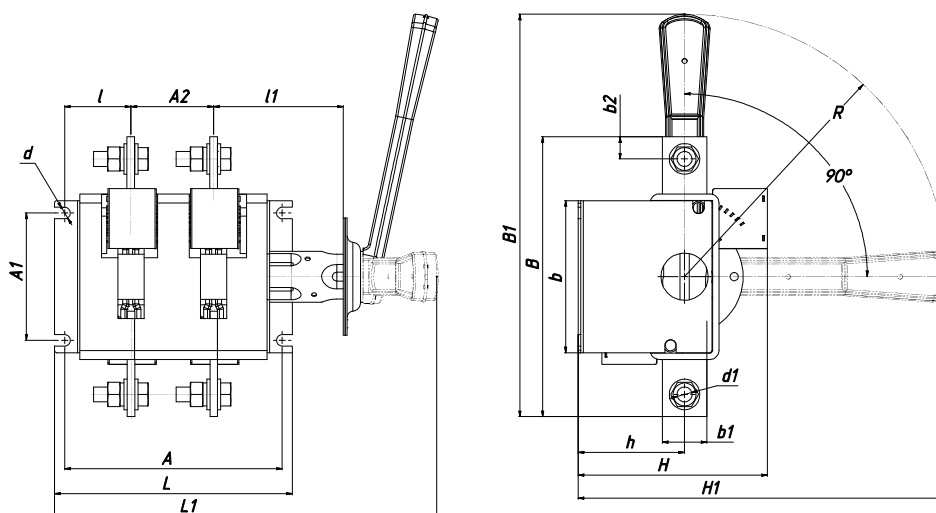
Выключатель-разъединитель на одно направление двухполюсный с боковой смещенной ручкой
